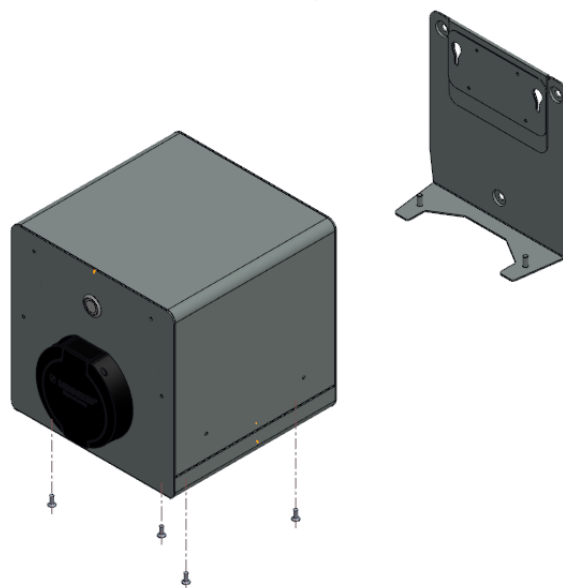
SlimBox mit demontierter Wandhalterung und demontierten Befestigungsschrauben des Gehäusedeckels
